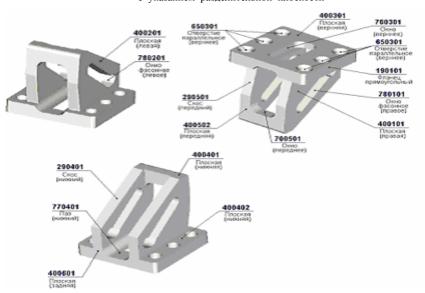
Кодирование поверхностей корпусной детали «Кронштейн»
